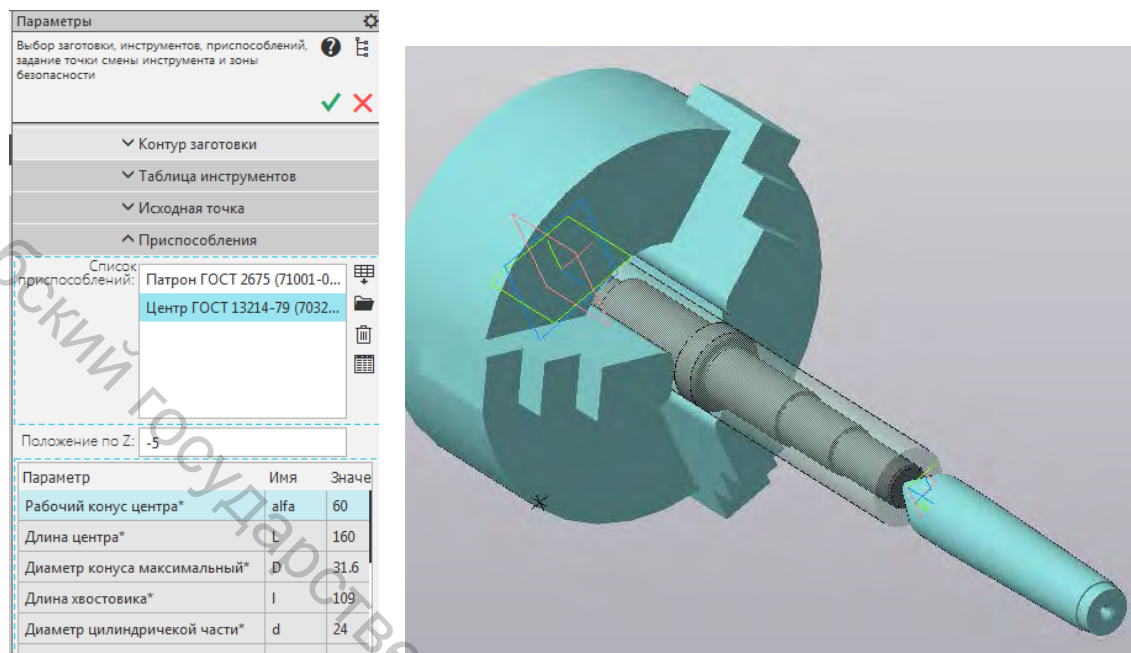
Использование центра для обработки вала при отношении длины к диаметру больше пяти
